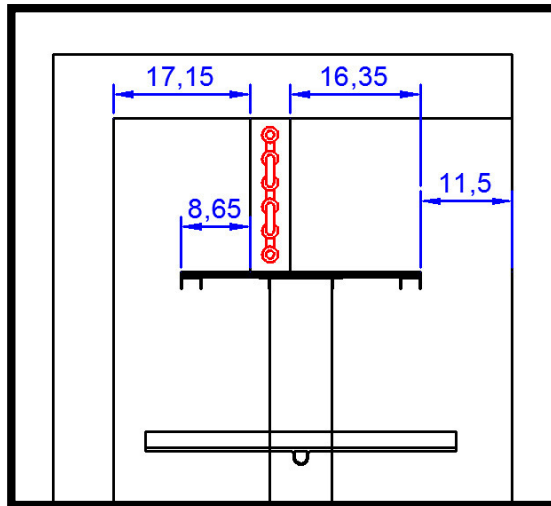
Vista lateral de las medidas para la colocación del elemento calefactor.
